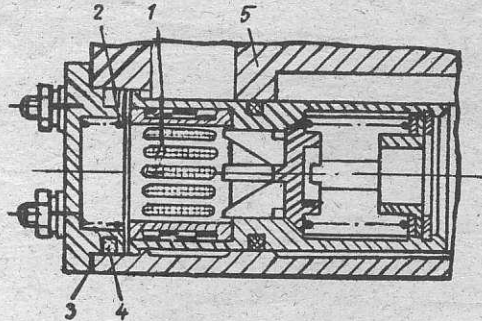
Druckminderventil des oberen Schmierstoffaggregates
